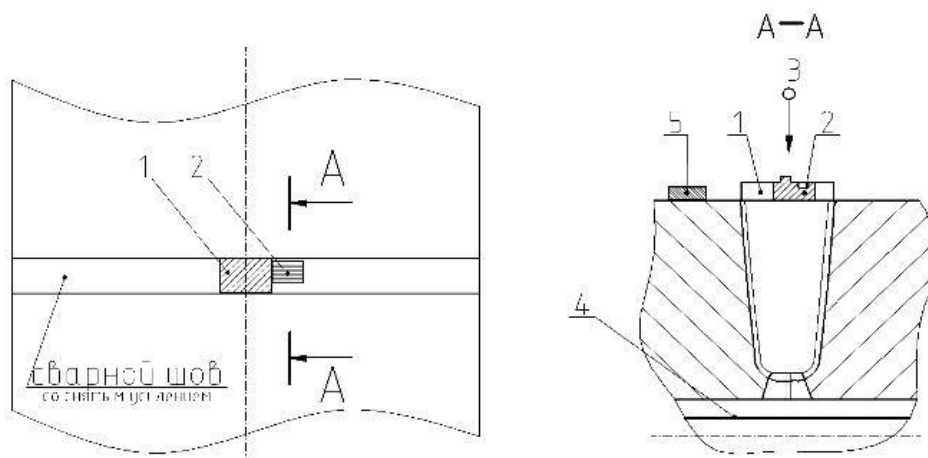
Схема контроля утяжки и проплава корня сварного шва со снятым валиком усиления:
